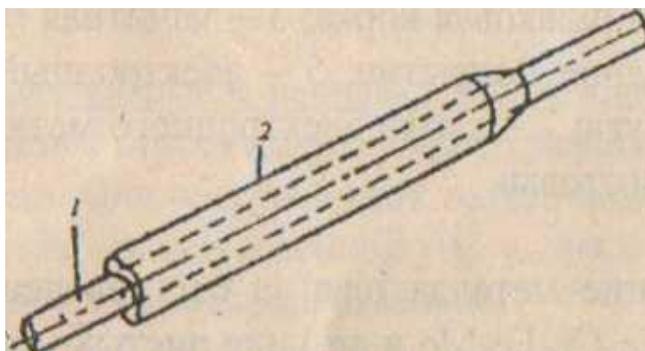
Сварочный электрод: 1 - стержень; 2 - покрытие
